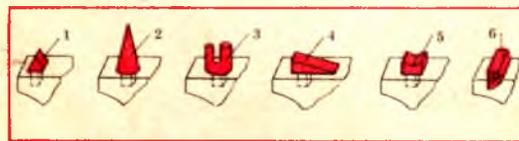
Подкладной инструмент, устанавливаемый на наковальне: 1 — просечки; 2 — конусные оправки; 3 — вилка; 4—6 — оправки
